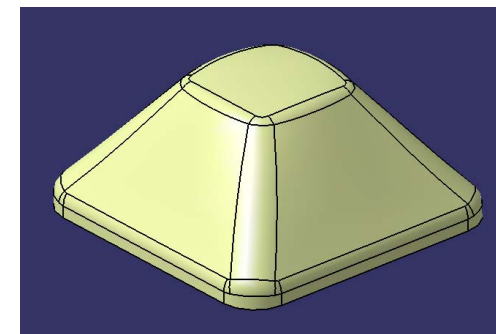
Spojení vrchlíku s bočními stěnami R=5mm
